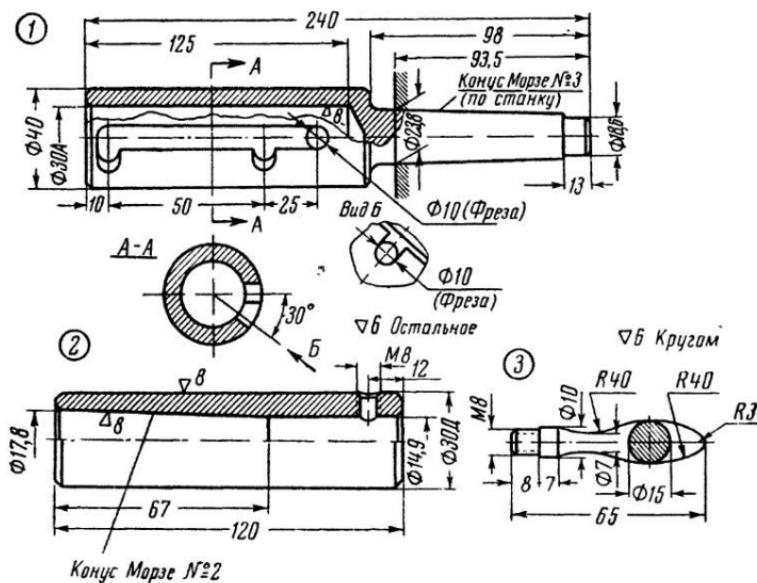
Детали сверлильного пистолета: 1 — корпус; 2 — втулка; 3 — ручка.
